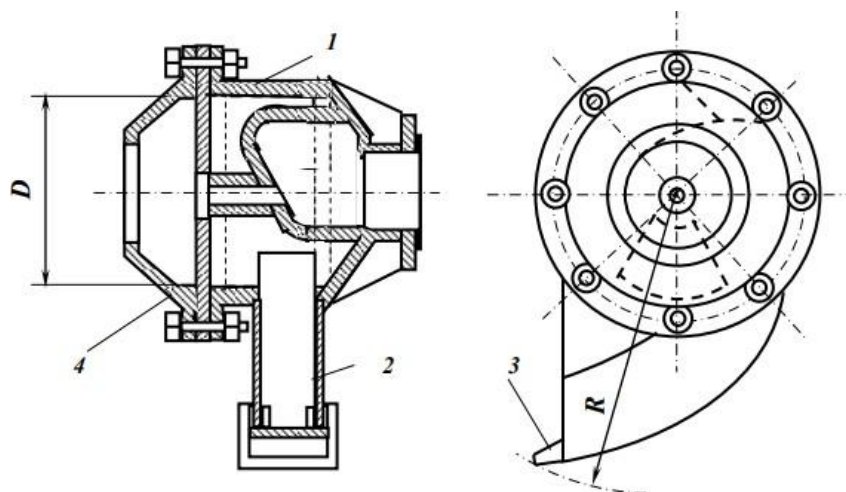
Комбінований живильник. 1-корпус; 2-черпак; 3-козирок черпака; 4-кришка.
